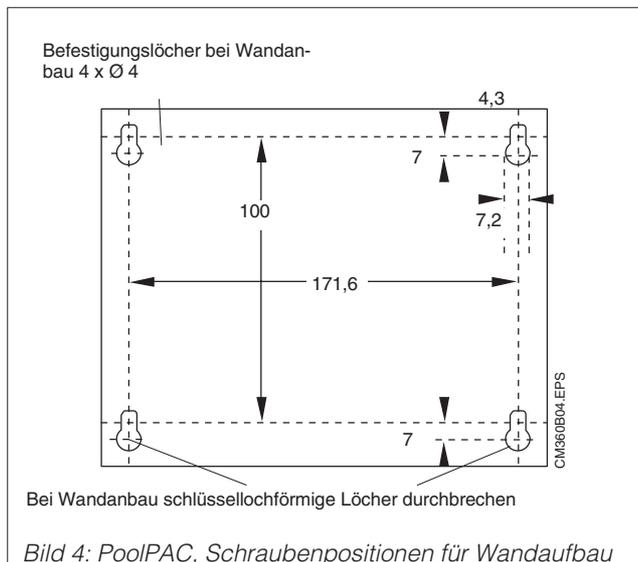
PoolPAC, Schraubenpositionen für Wandaufbau
